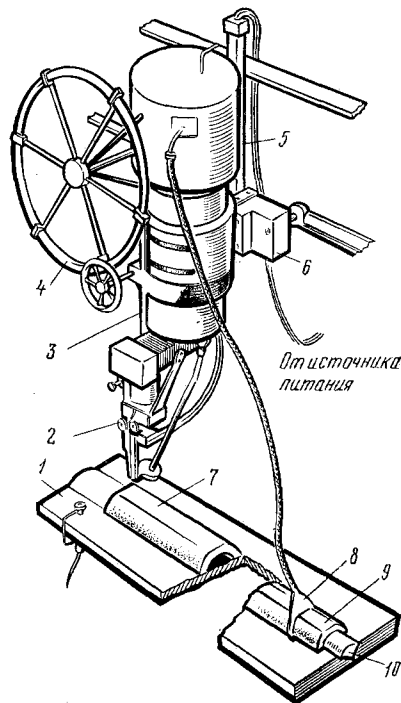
Схема установки для автоматической электродуговой сварки металла под флюсом:
